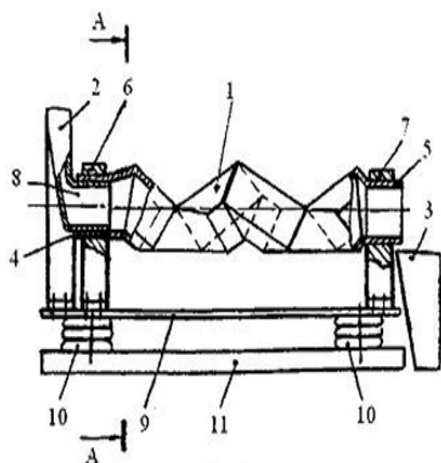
Установка для смешивания сыпучих материалов, вид спереди
